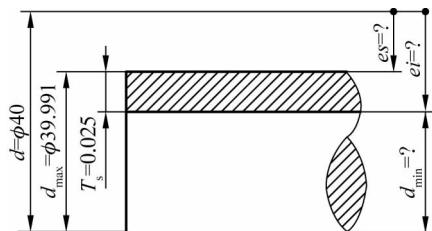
轴的极限尺寸、极限偏差与公差计算
